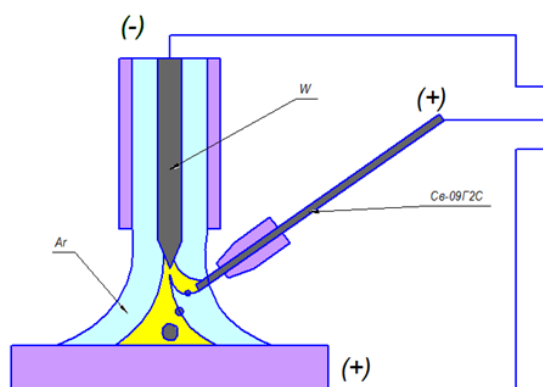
Сущность способа сварки разветвлённой дугой
